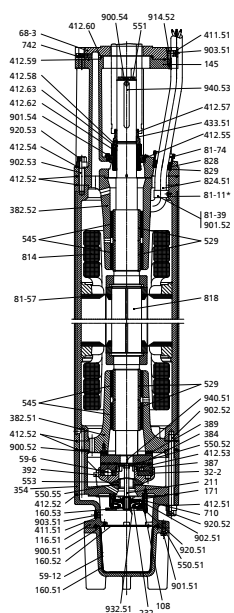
Компонировочный чертеж погружного двигателя V, X
